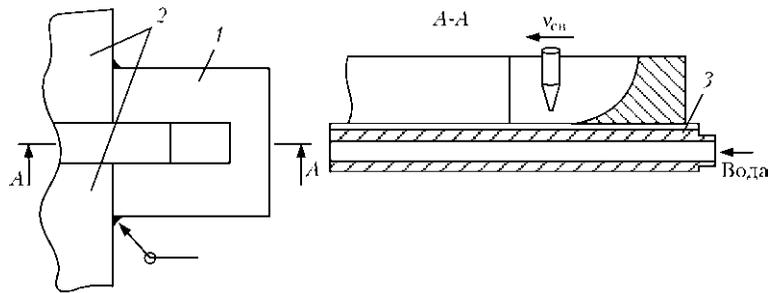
Схема выполнения сварки с выводной планкой: 1 — выводная планка; 2 — свариваемые плиты; 3 — формирующая подкладка
